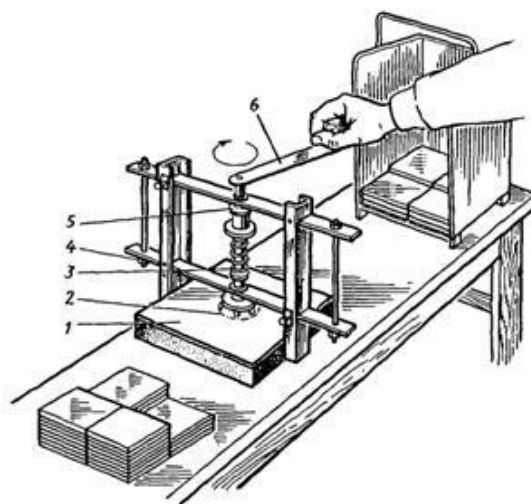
Организация рабочего места при высверливании отверстий с помощью приспособления с вращающимся резцом:
